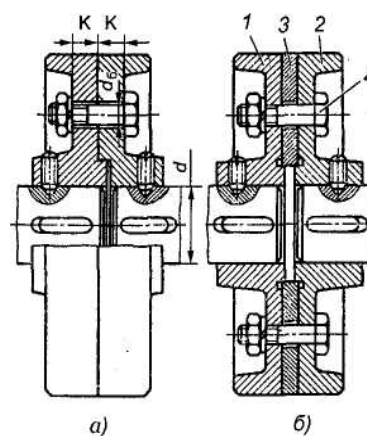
Фланцевые муфты: а – центровка за счет выступа; б – центровка кольцом
